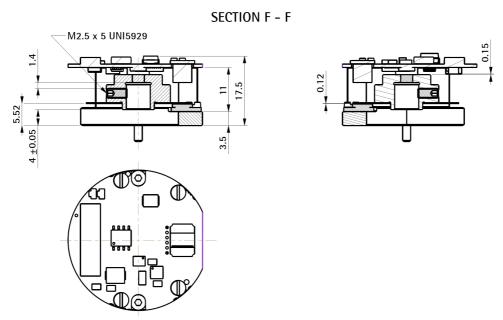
Dimensioni di ingombro dell'encoder - Sezione F - F
